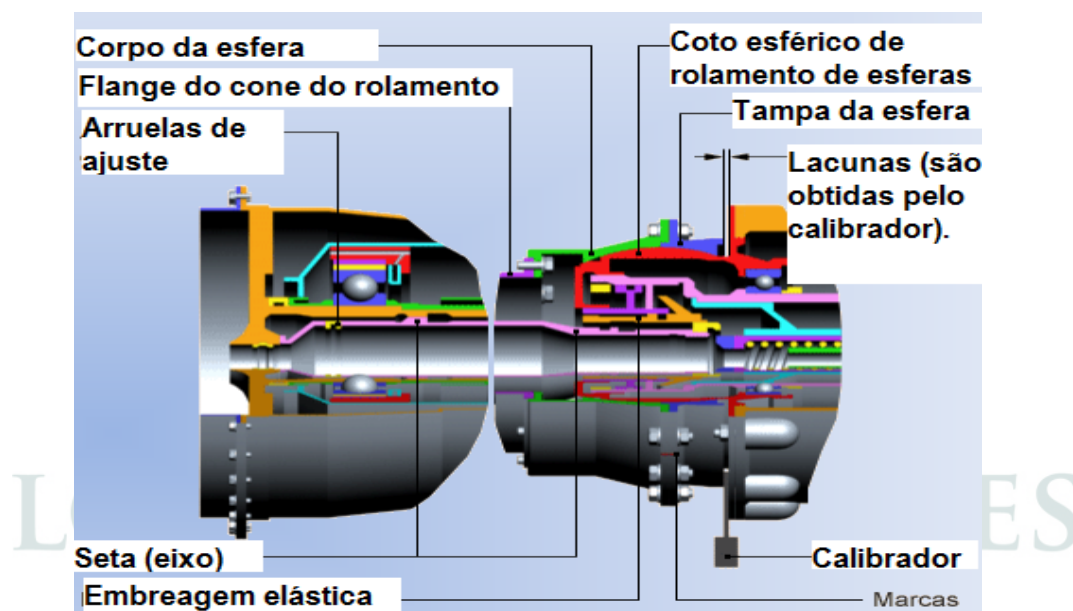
Fixação traseira do motor TV3-117VM.
